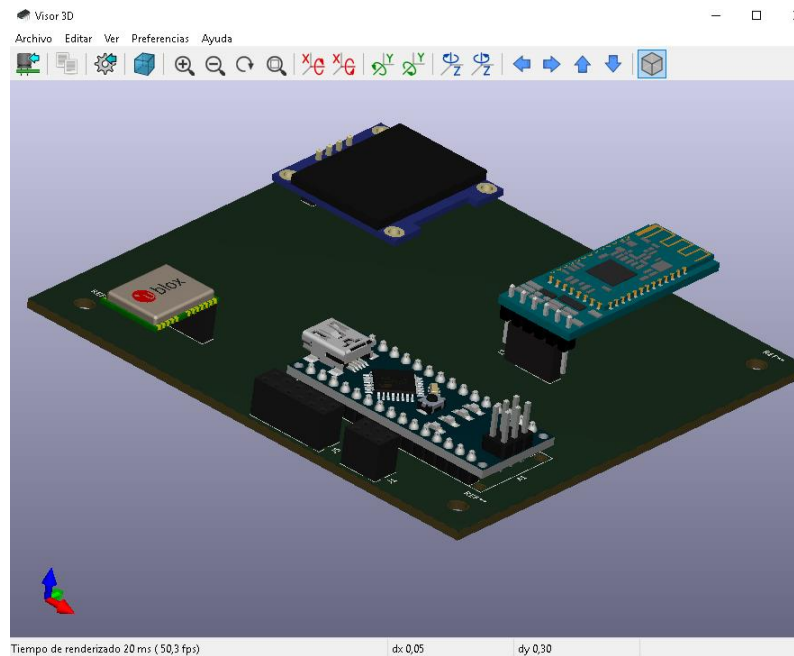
Vista posterior PCB en 3D Viewer KiCAD
